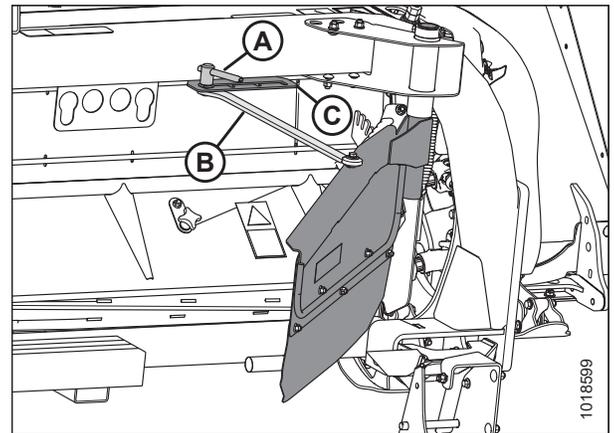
Боковой дефлектор правого формовочного щитка
